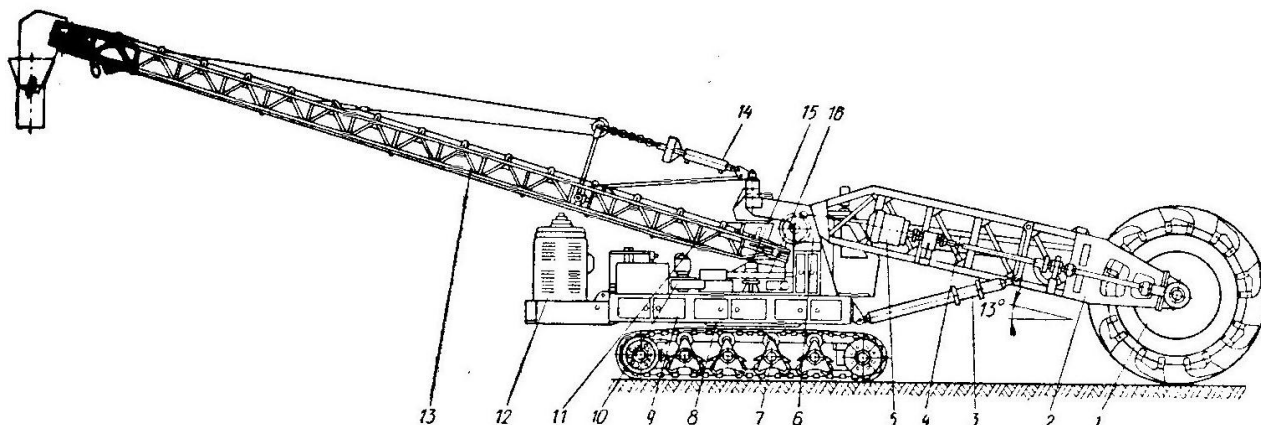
12. Общий вид роторного экскаватора: 1 – ротор с ковшами; 2 – стрела; 3 – гидроцилиндр наклона стрелы; 4 – приемный транспортер; 5 – привод ротора; 6 – портал стрелы; 7 – гусеничный движитель; 8 – ОПУ; 9 – поворотная платформа; 10 - привод поворота; 11 – корневая секция отвального транспортера; 12 – силовая установка; 13 – наклоняемая секция отвального транспортера; 14 – привод наклона транспортера; 15 – портал отвального транспортера; 16 – привод поворота отвального транспортера
